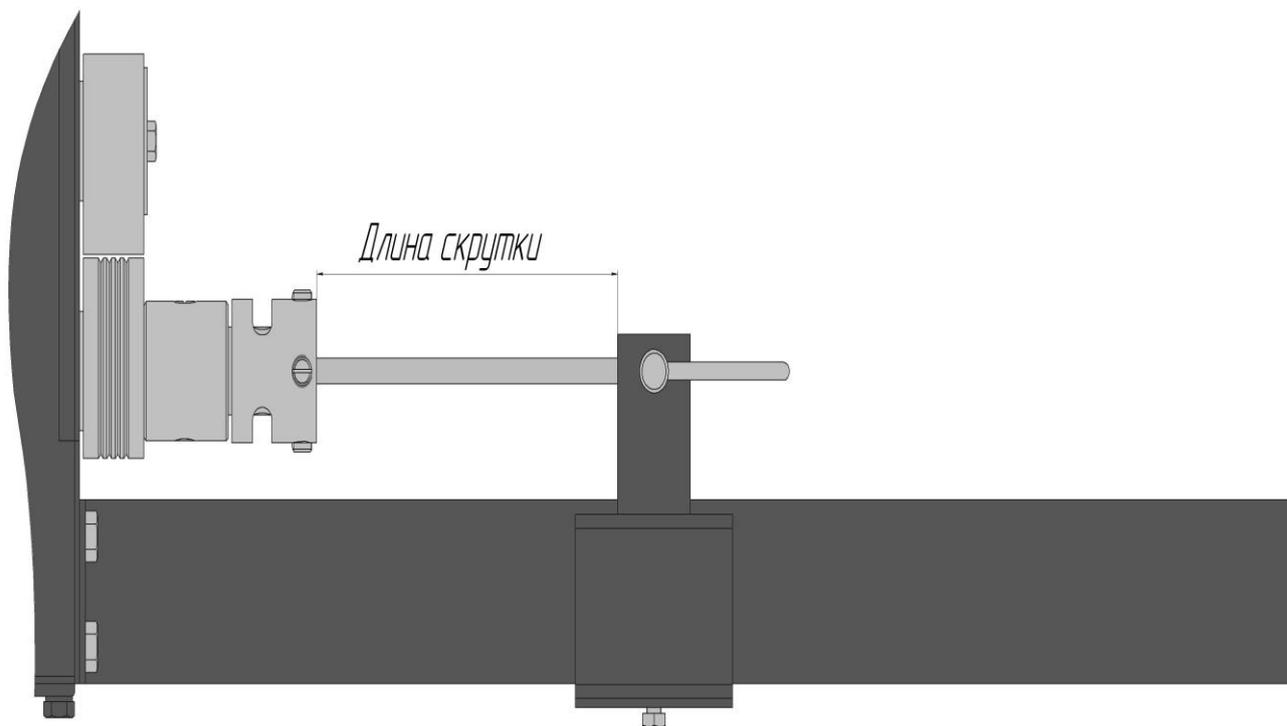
Монтаж дополнительных приспособлений для операции продольного скручивания прутка металлопроката.
